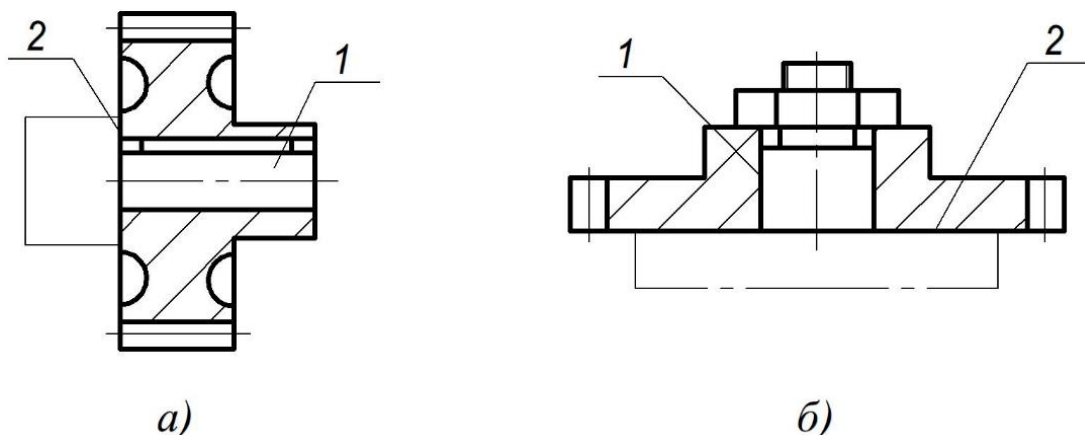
Схема основних конструкторських (а) і технологічних (б) баз зубчастих коліс: 1 – базовий отвір колеса; 2 – базовий торець колеса
